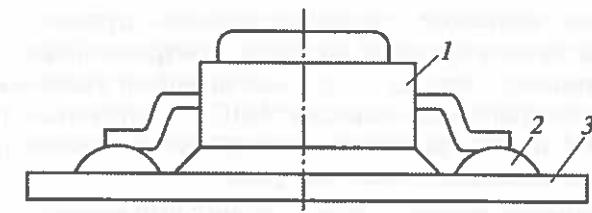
Установка ИМС с планарными выводами на печатной плате без зазора:
